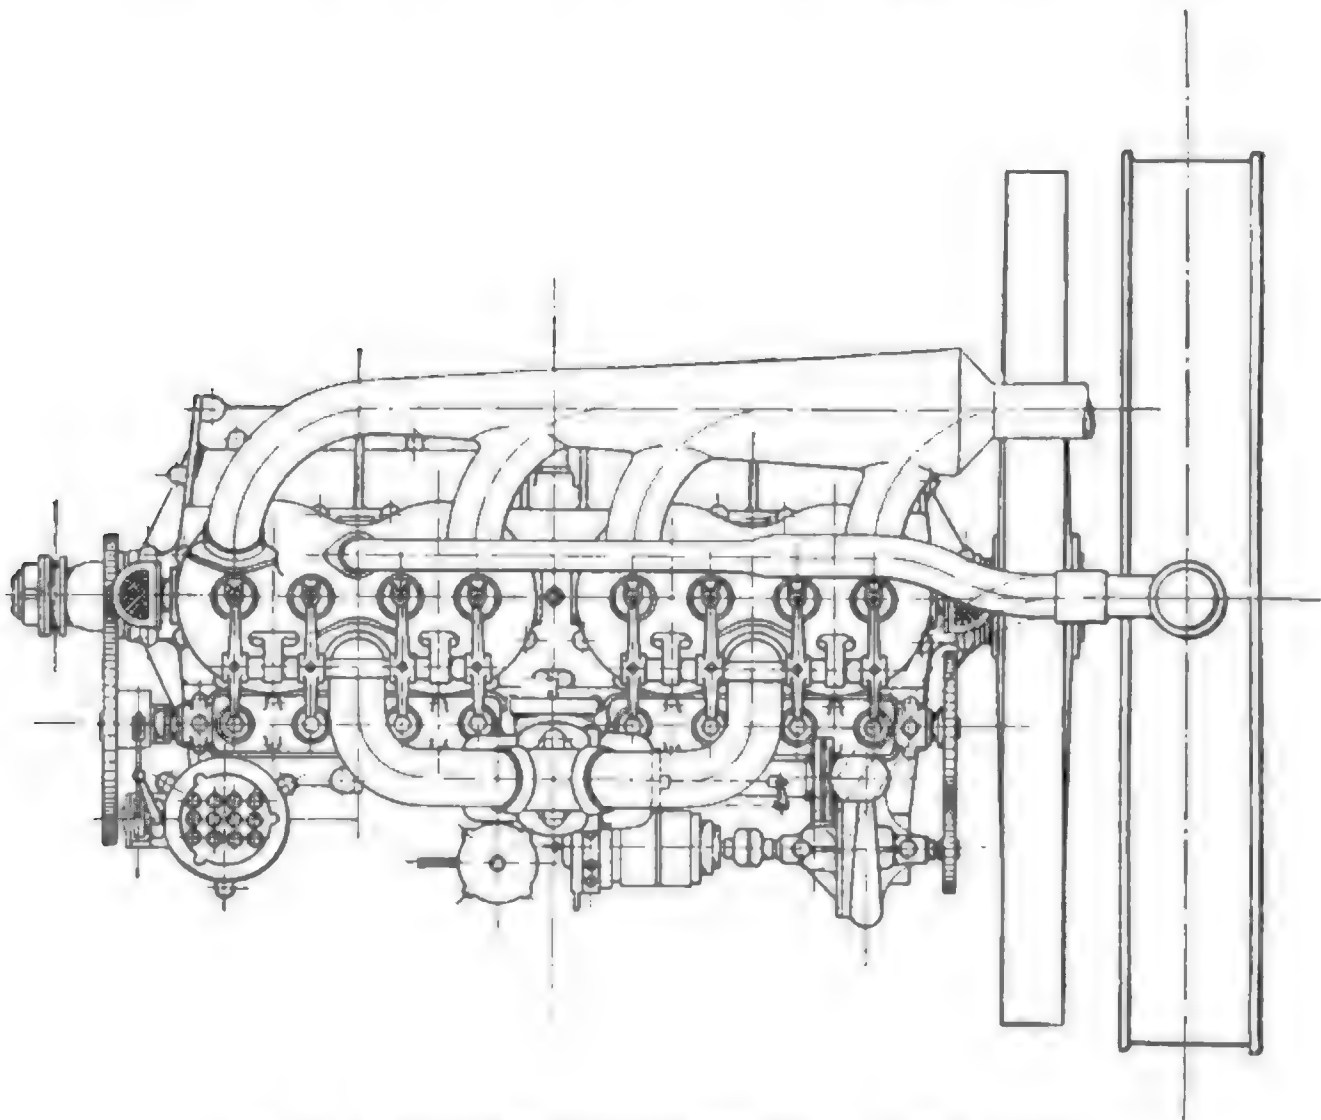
Zeichnung des Flugmotors der Daimlerwerke. Ansicht von oben.
